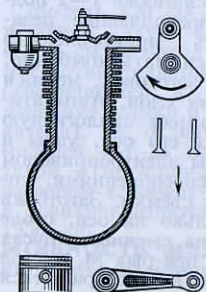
Мультипликационные заготовки для съёмки технического сюжета: а — собранная заготовка; б — элементы заготовки.
